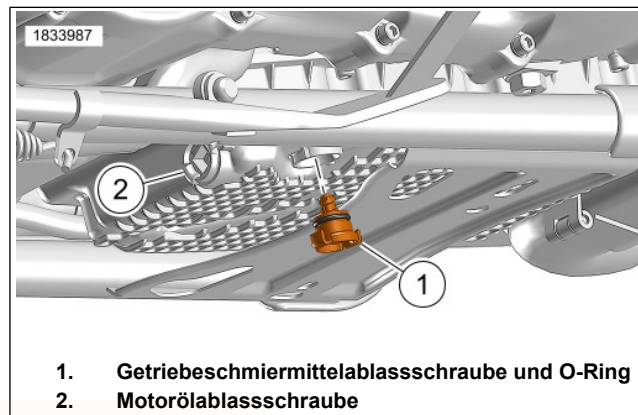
Getriebeschmiermittelablassschraube PRIMÄRKETTENGEGHÄUSESCHMIERMITTEL WECHSELN
